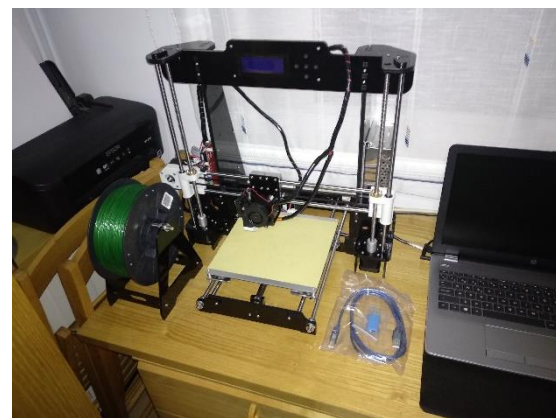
Impresora Anet A8 montada. Fuente: Autor.
